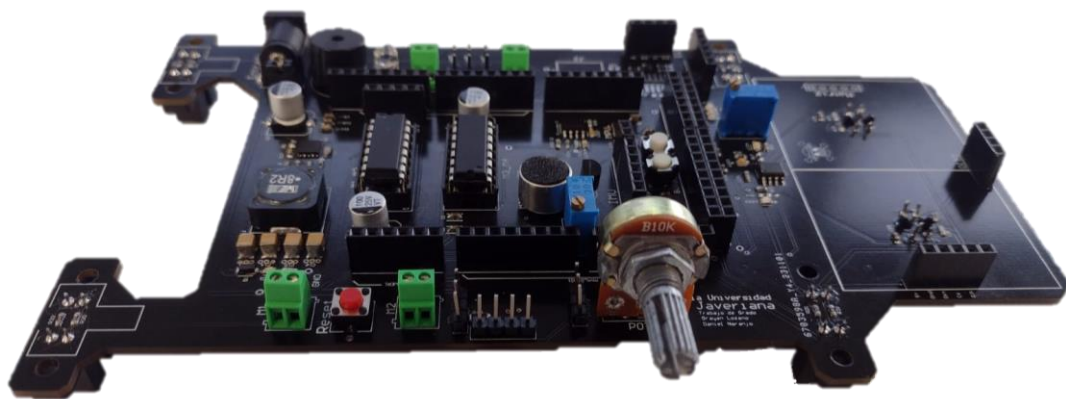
Vista lateral del PCB Versión 3 con componentes soldados
